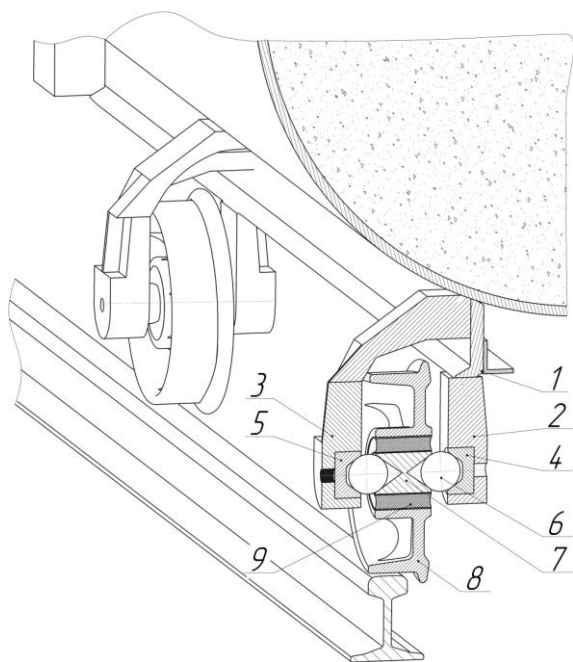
Принципова конструкція буксового вузла з додатковою рухливістю колеса: 1 – лонжерон; 2, 3 – поводки; 4, 5 – упорні втулки; 6 – шар; 7 – упорно-направляюча втулка; 8 – колесо; 9 – пружно-дисипативний елемент
